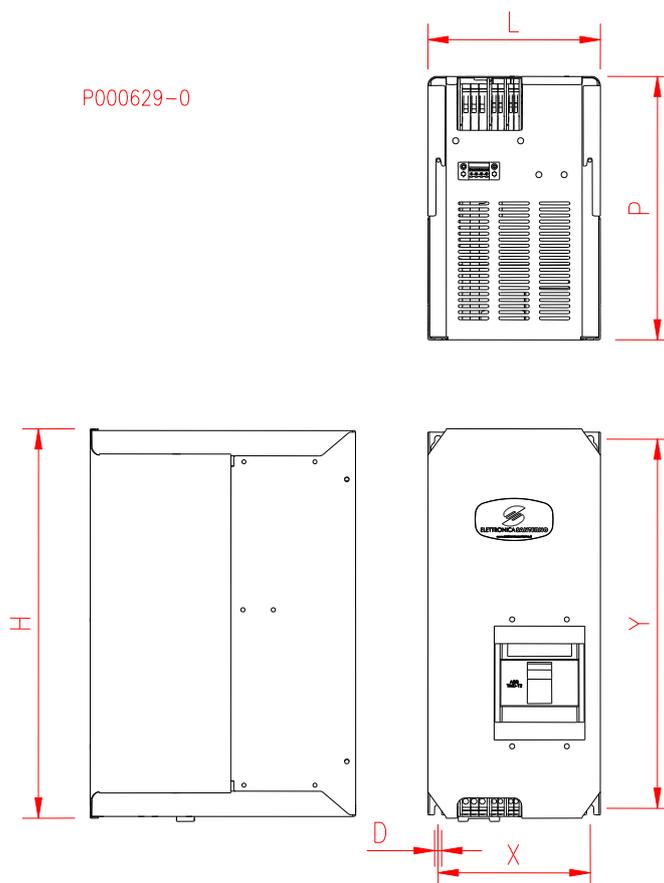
Dimensioni e fori di fissaggio del pannello di interfaccia
